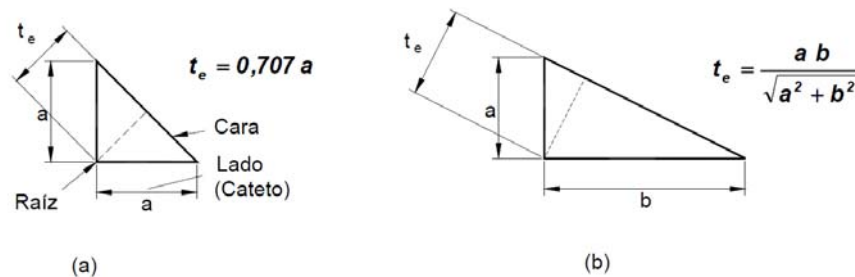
Sección transversal de soldadura. Extraída de los comentarios del CIRSOC 301/05
